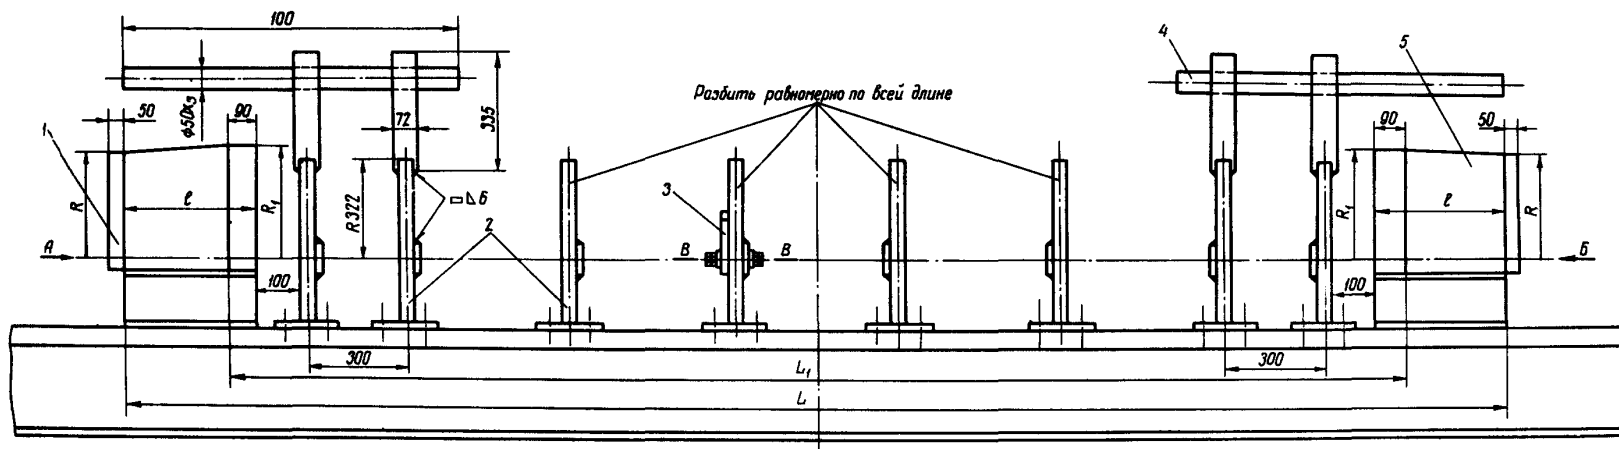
I. Макет для пайки, необходимые детали и размеры (мм)
